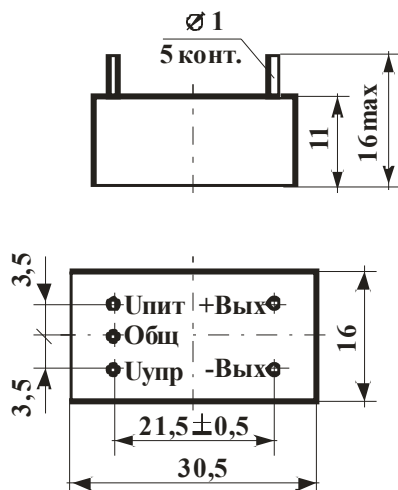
Габаритный чертёж модулей МТКН
